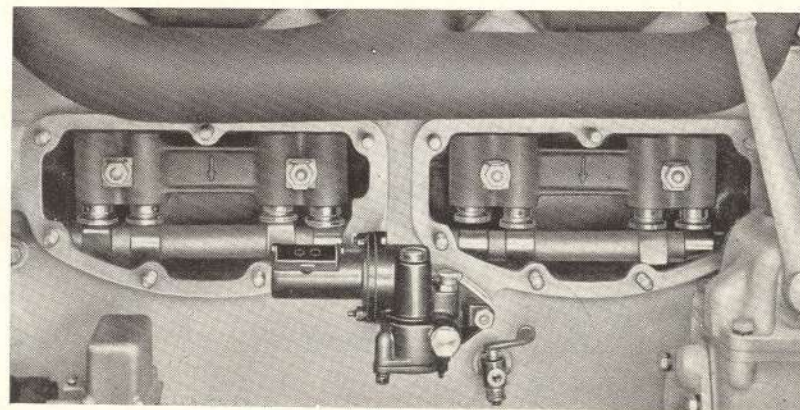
Position des cames pour le balancement des soupapes du cylindre N. 1. Soupape d'admission = début d'ouverture - Soupape d'échappement = fin de fermeture.
